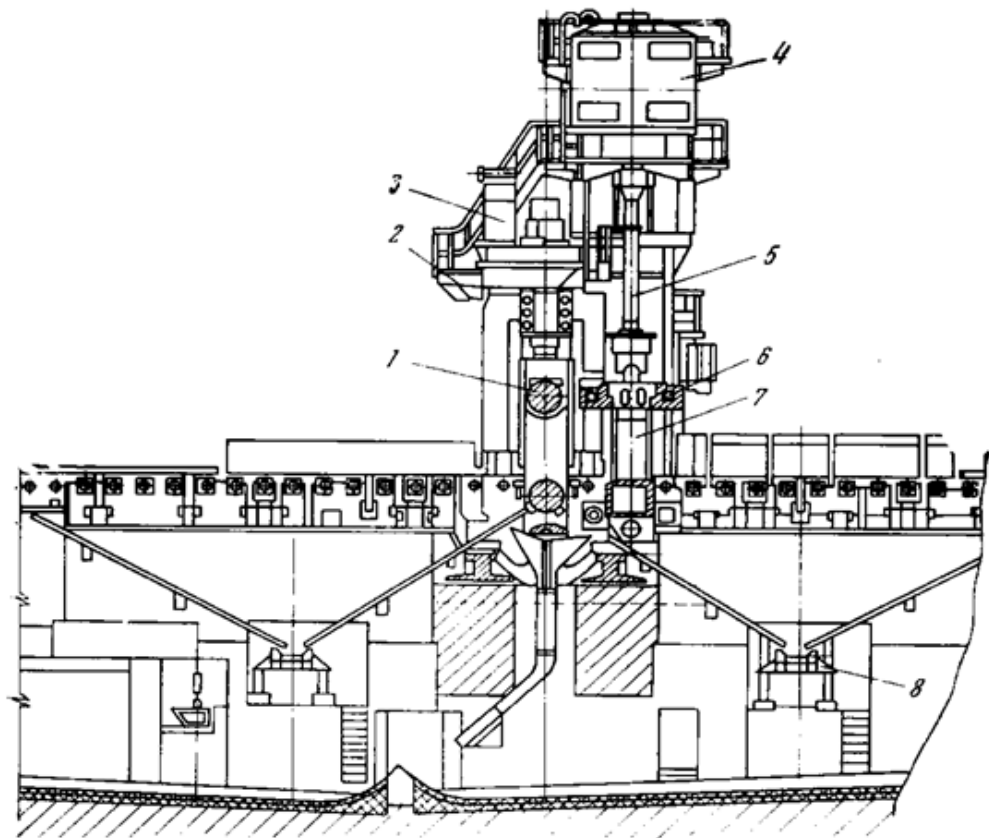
Загальний вид робочої кліті слябінга 1150
